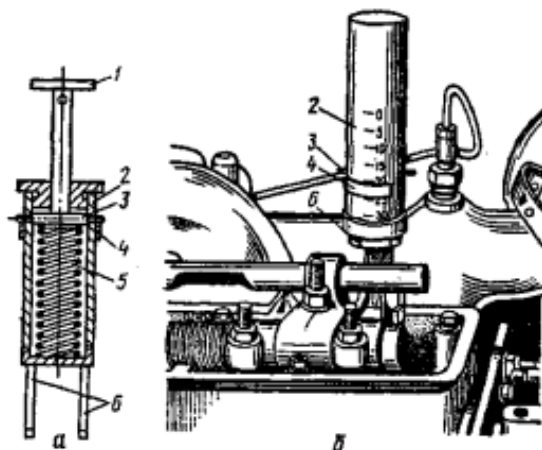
Перевірка пружності пружини клапанів газорозподілу приладом КИ-723: а – прилад для перевірки зусилля притискування клапанів до сідел головки циліндрів; б – визначення зусилля притискування клапану до сідла; 1 – рукоятка приладу; 2 – корпус; 3 – натискний штифт; 4 – кільце-фіксатор; 5 – пружина; 6 – встановлювальні стійки.
